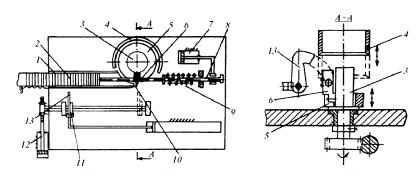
Схема механизма сборки заготовок лепестковых кругов; I- желоб; 2- толкатель лепестков; 3- сердечник; 4- форма; 5- толкатель; 6- упор;  $7,\ I2-$  пневмощилиндры; 8- шток; 9- пружина; I0- гибкии элемент; II- каретка; I3- отсекатель
